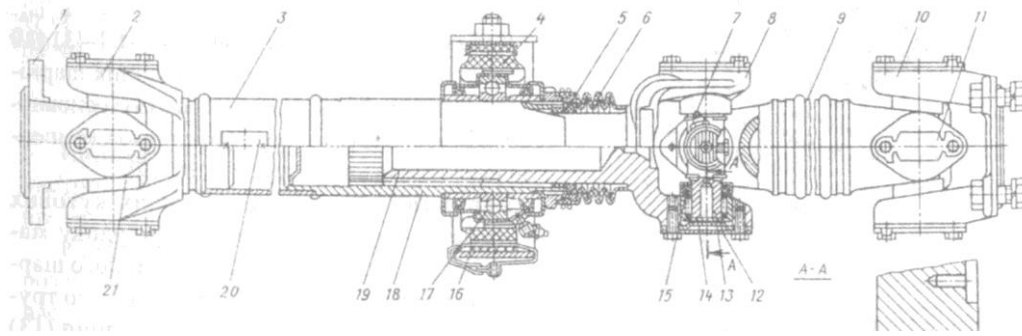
Карданна передача автомобіля ЗИЛ: 1 і 2 - вилки карданного шарніра; 3 і 9 - проміжний і основний вали; 4 - гумова обойма; 5 і 6 - ущільнення і чохол; 7 - маслянка; 8, 10 і 2! - карданні шарніри; 11 - шайба; 12 - голчасті підшипники; 13 - шипи хрестовини; 14 - кришка; 15 – комбіноване ущільнення; 16 - проміжна опора; 17 - підшипник проміжної пори; 18 і 19 - шліцьове з'єднання; 20 - балансувальні пластини
